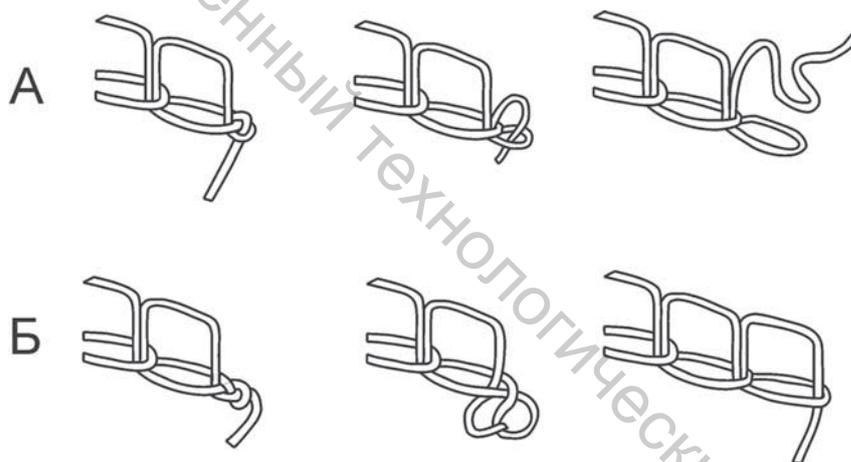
Схемы изготовления узла для однониточного цепного стежка
